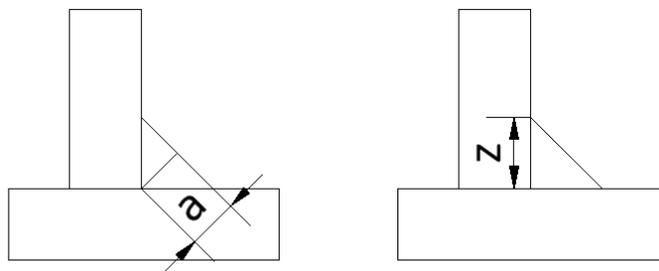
Dimensión transversal de una soldadura en ángulo
